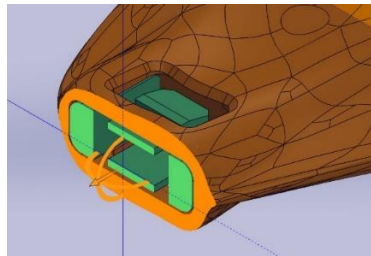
Mecanismo de encaixe do tipo macho e fêmea para acoplamento dos componentes coto e palmar
